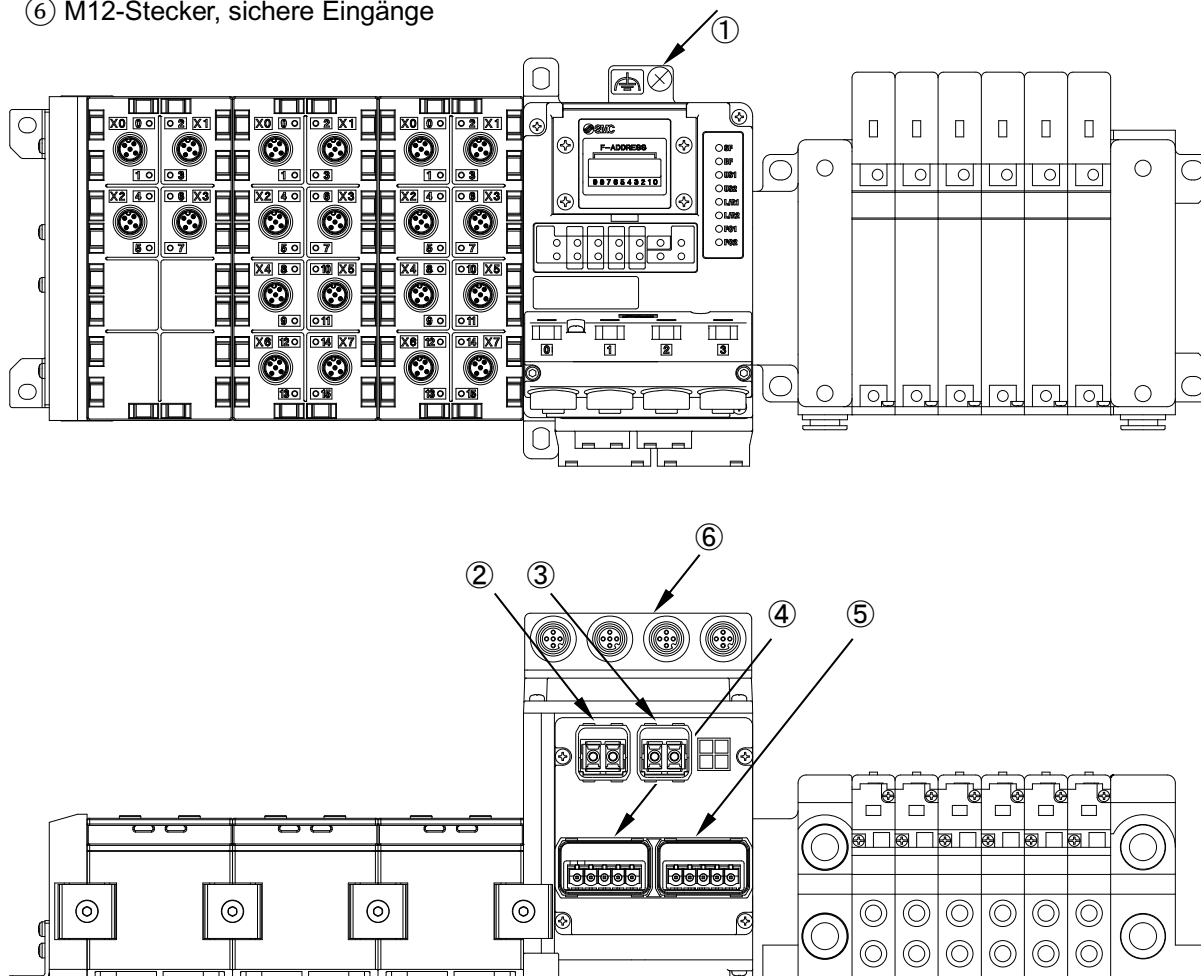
Anordnung der Schrauben und Stecker (EX245-FPS1/2)
